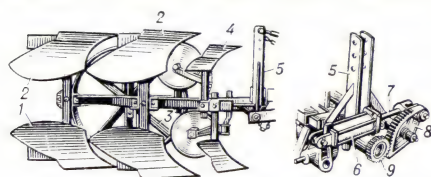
Оборотный навесной плуг: 1 — правооборачивающий корпус; 2 — левооборачивающий корпус; 3 — опорное колесо; 4 — левооборачивающий предплужник; 5 — навеска плуга; 6 — гидроцилиндр поворота; 7 — шток; 8 и 9 — механизм поворота плуга.
